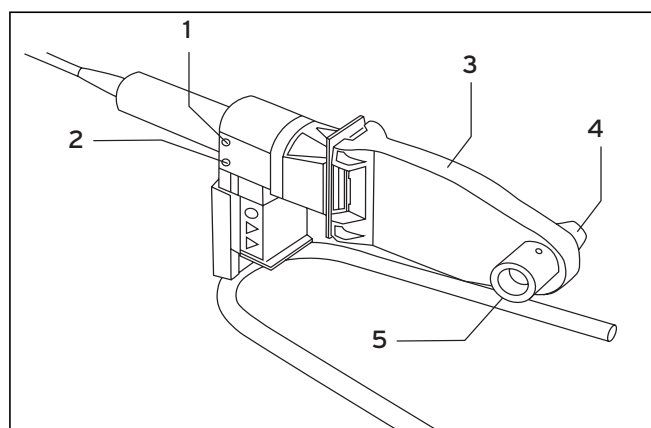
Benötigte Werkzeuge (2 von 2)
